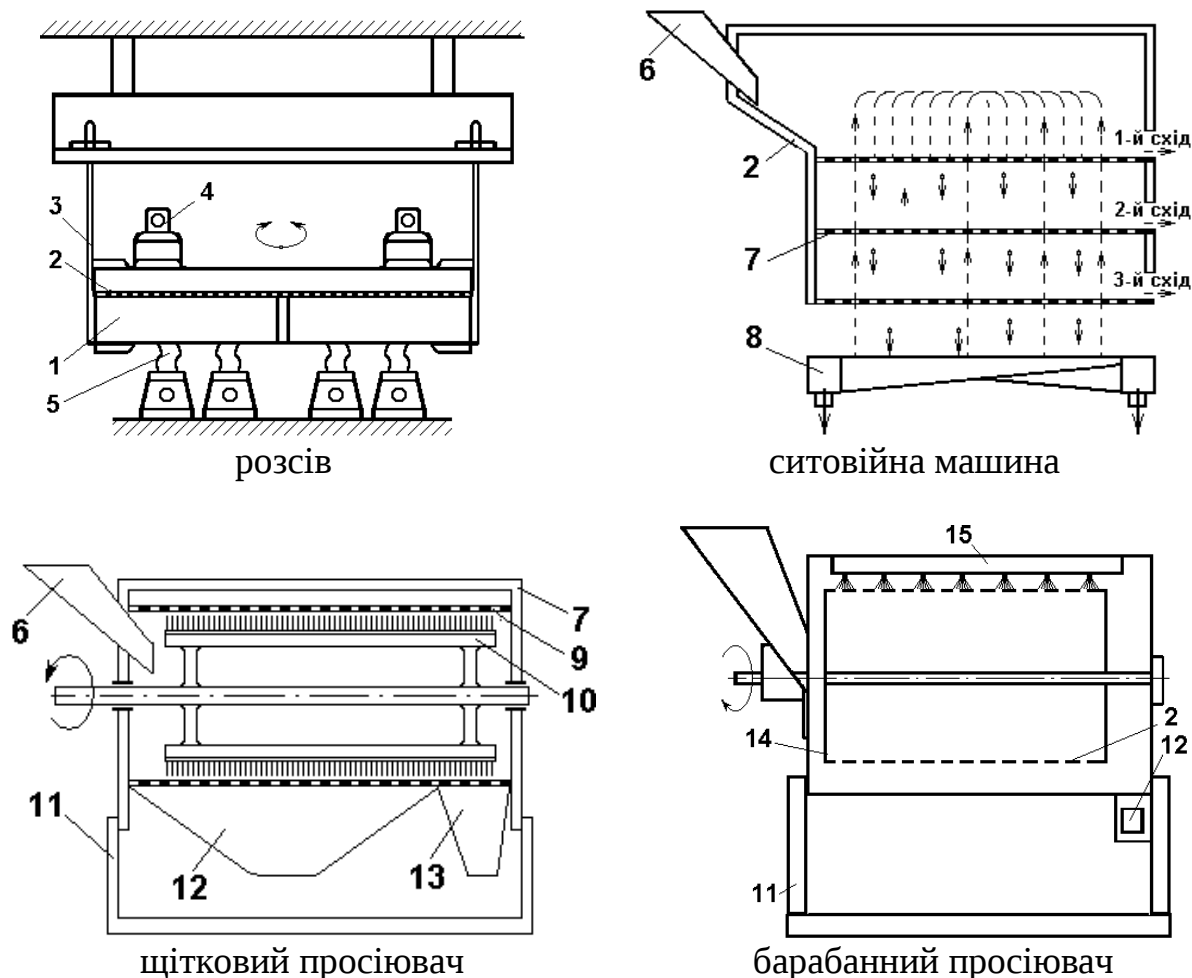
Конструктивно-технологічні схеми просіювачів: 1 – ситова рама; 2 – сито; 3 – трос; 4 – приймальний рукав; 5 – випускний рукав; 6 – лійка; 7 – корпус; 8 – вивантажувальний короб; 9 – решето; 10 – щітковий барабан; 11 – рама; 12 – вивантажувальне вікно; 13 – вивантажувальна горловина; 14 – барабан; 15 – щітка
